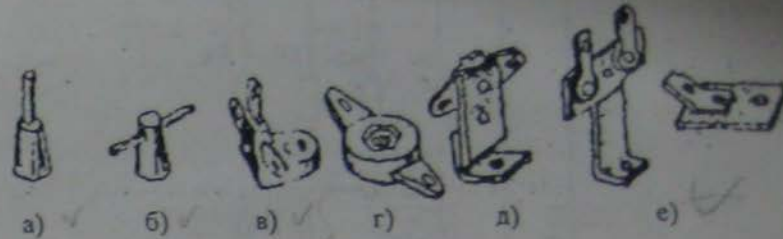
Варианты опорных приспособлений для навесного монтажа
